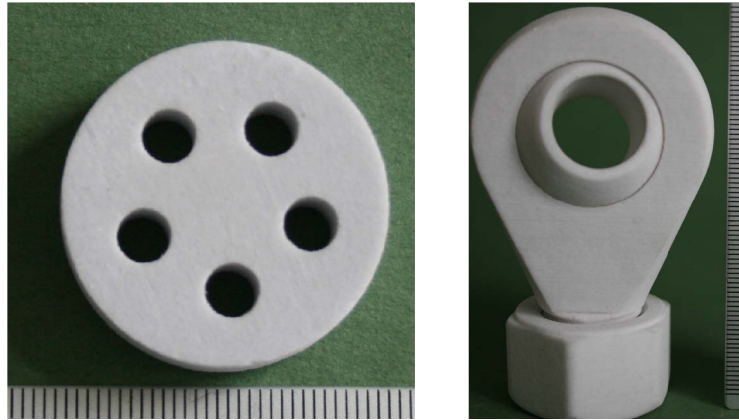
links: 3D - gedrucktes Modell für einen Sinterglaskörper, rechts: Maschinenteil Kugelkopf (Material: Gipskeramik)
